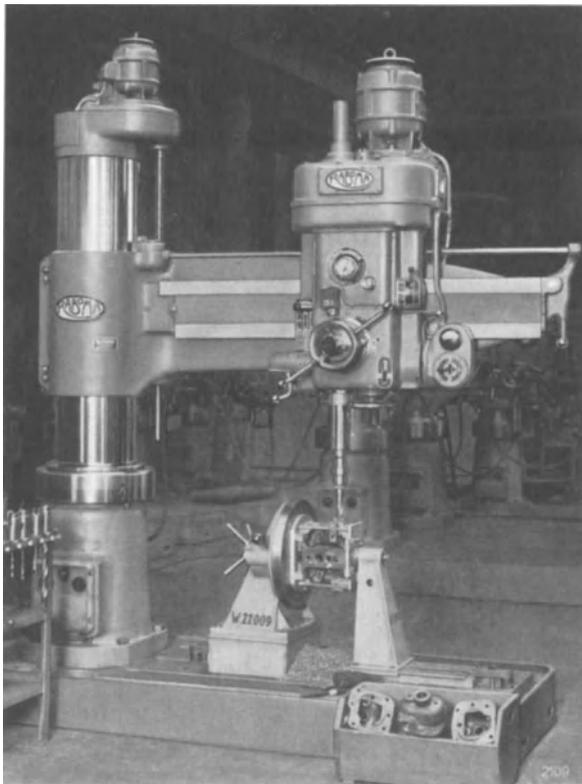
Schwenkvorrichtung mit angeflanschem Bohrkasten
